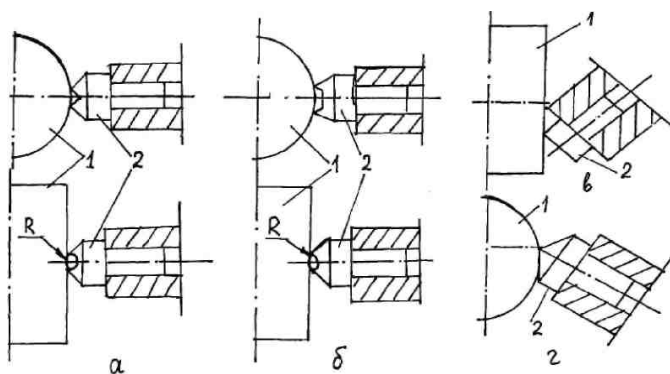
Схемы установок выглаживателей при обработке цилиндрической поверхности: 1 — обрабатываемая поверхность; 2 — заточка (а — сферическая форма заточки; б — цилиндрическая; в — тороидальная; з — коническая)
